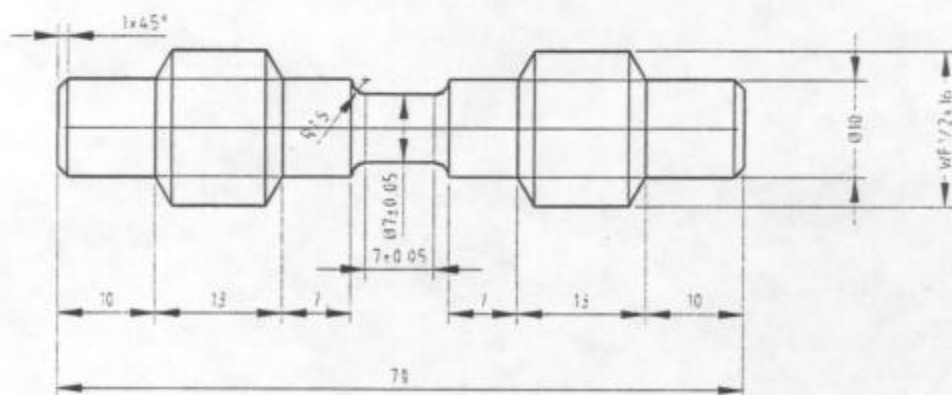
Dimensiones de la probeta de torsión en caliente.
